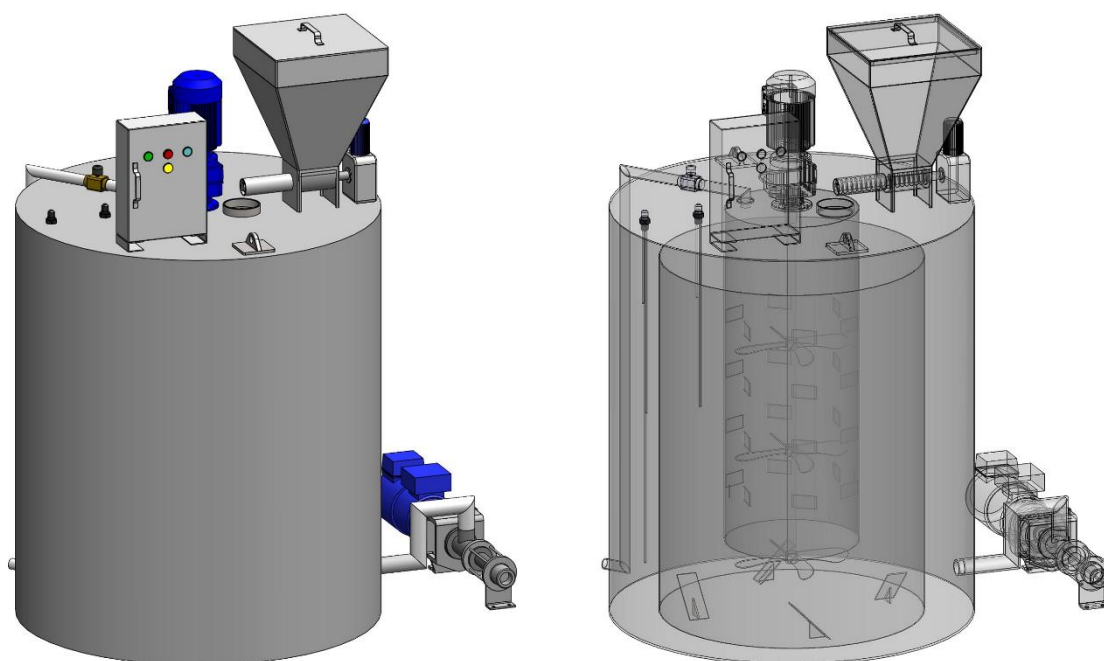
3D-модель мехатронной установки для приготовления раствора флокулянта.
